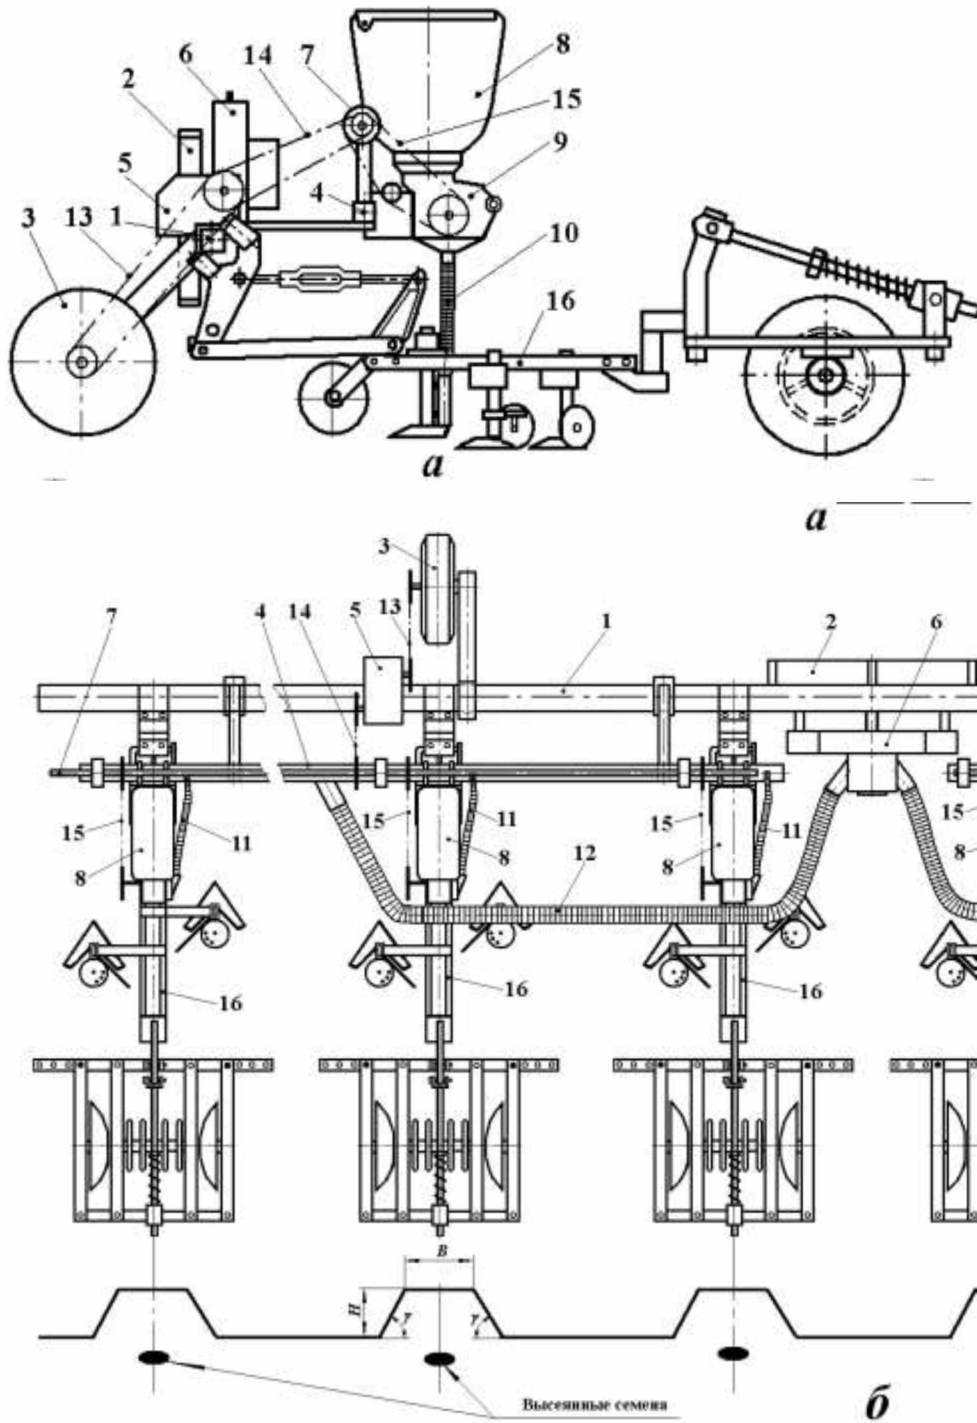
Гребенева сівалка: а - вид збоку; б - вид зверху
